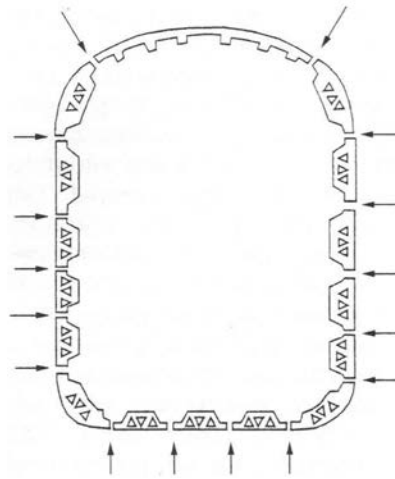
Конструктивно-технологическое членение кузова вагона из прессованных полых панелей (стрелками отмечены места сварки продольных швов)
